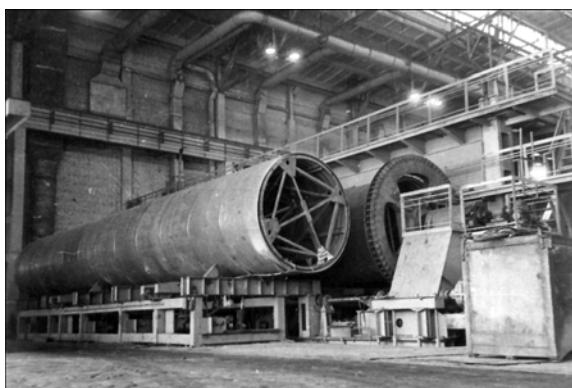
Стан для производства крупных сварных рулонируемых полотнищ, построенный на Новокузнецком заводе резервуарных металлоконструкций в 1974 г.
